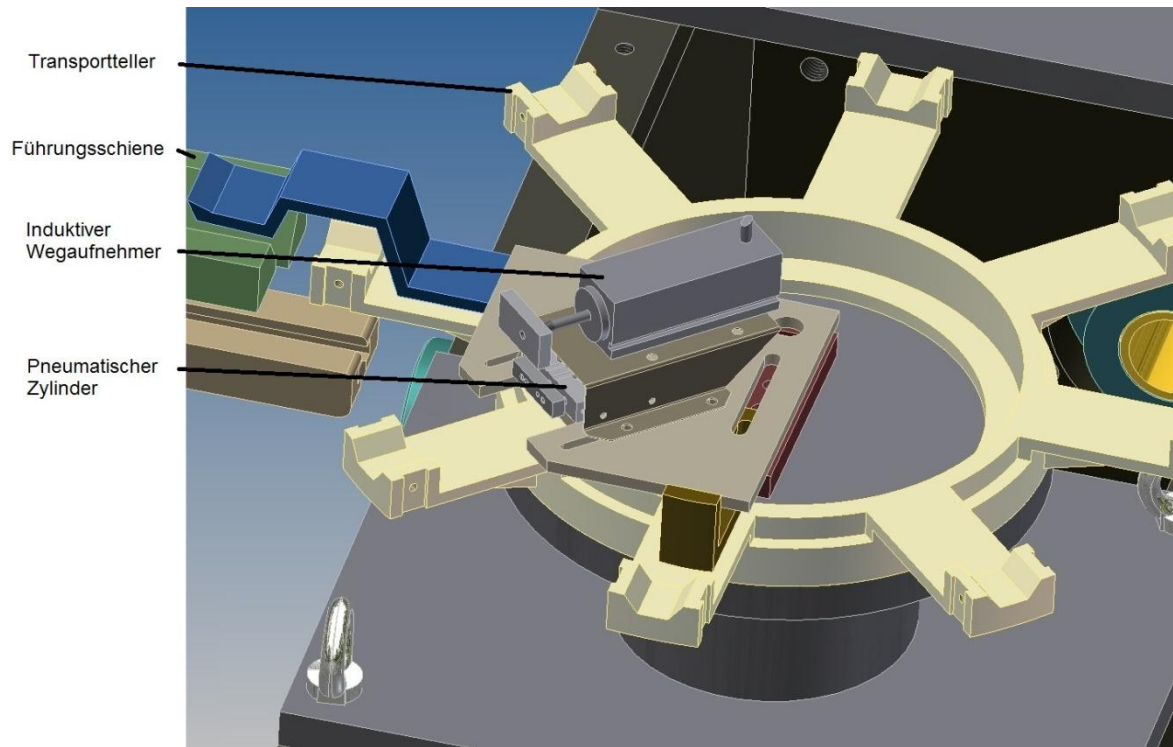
Längenmesssystem auf der Innenseite des Drehtellers
